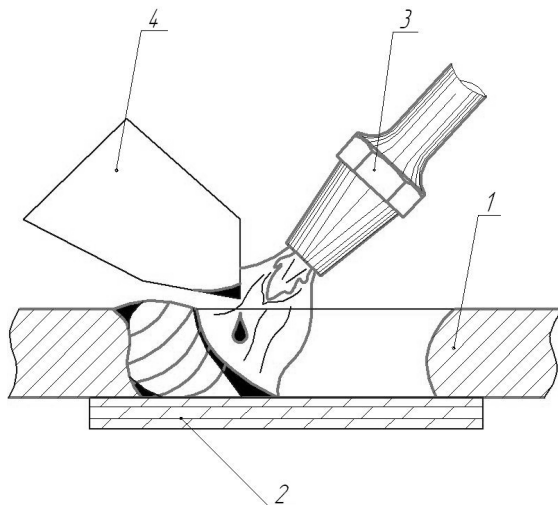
Устранение пробоины корпуса газовой сваркой: 1 – корпус с пробоиной; 2 – асбестовая прокладка; 3 – горелка; 4 – кусок силумина
